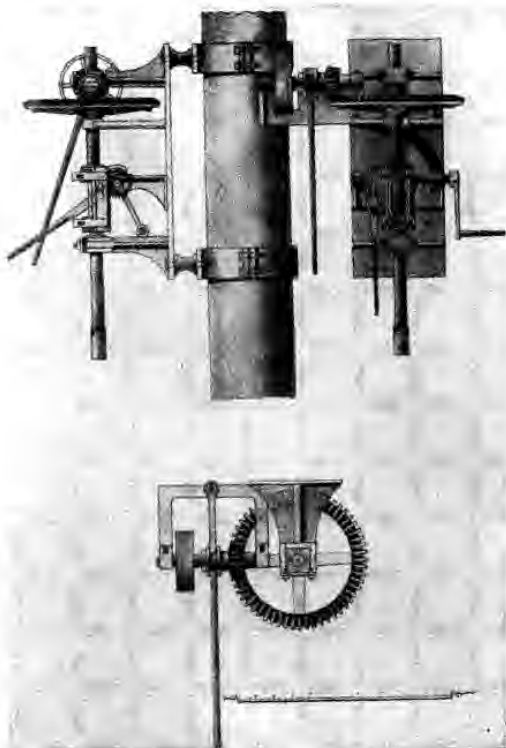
Двухшпindelный сверлильный станок Луганского завода.
